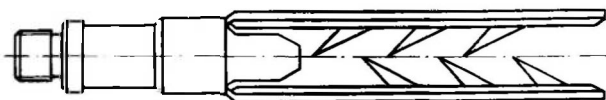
Инструмент типа "кошка" для ловли проволоки
